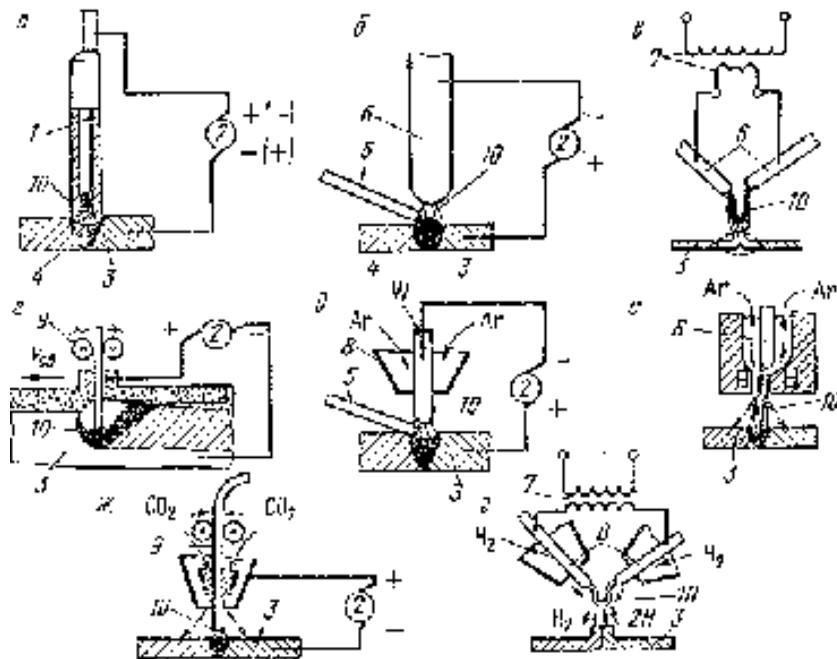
Схема процесса при использовании различных разновидностей электрической дуговой сварки: а – ручная дуговая сварка; б – автоматическая и полуавтоматическая сварка; в – аргонодуговая сварка; г – плазменная сварка; д – сварка в углекислом газе; з – атомно-водородная сварка
